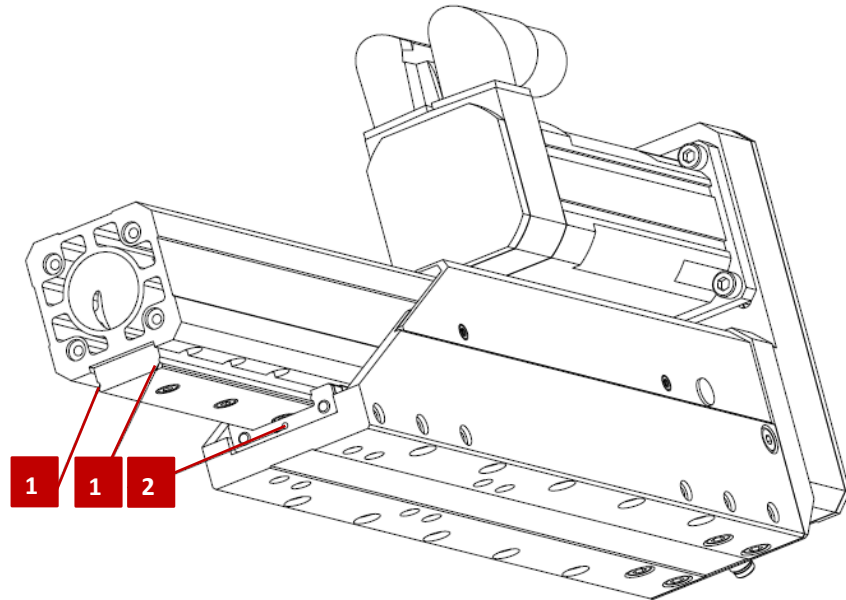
Spindelausleger – Schmiernippel Linearführung
